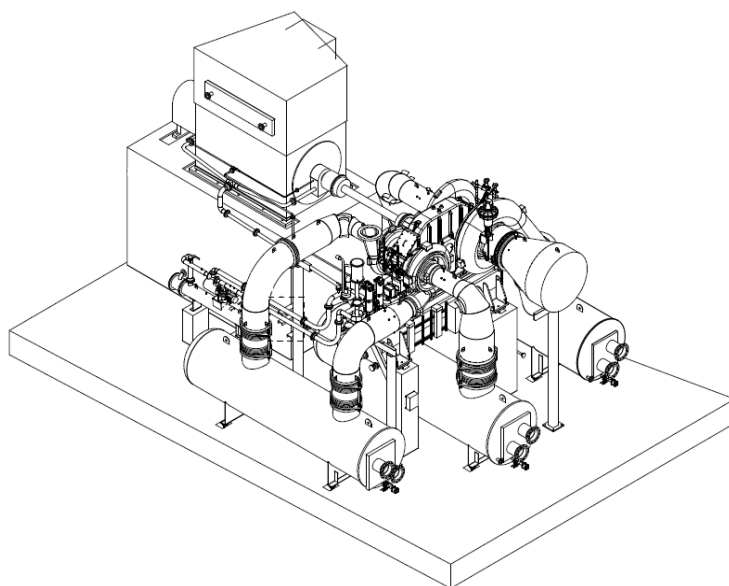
Modelo estrutural: vista isométrica do conjunto fundação-equipamento
